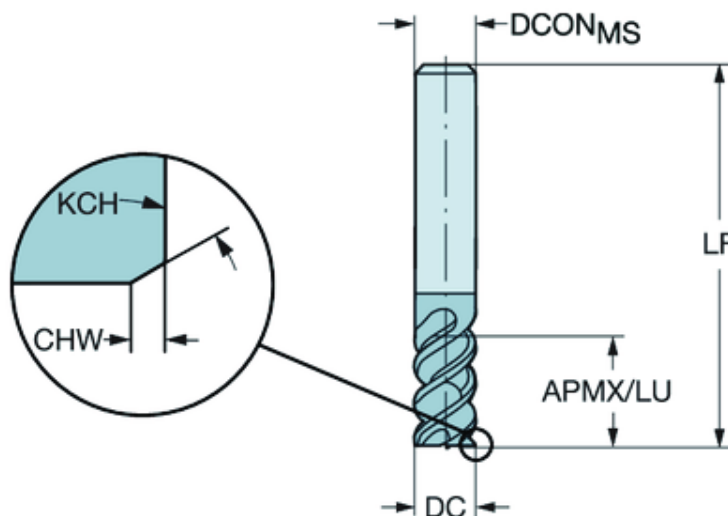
Фреза R216.34-06050-AK13P
